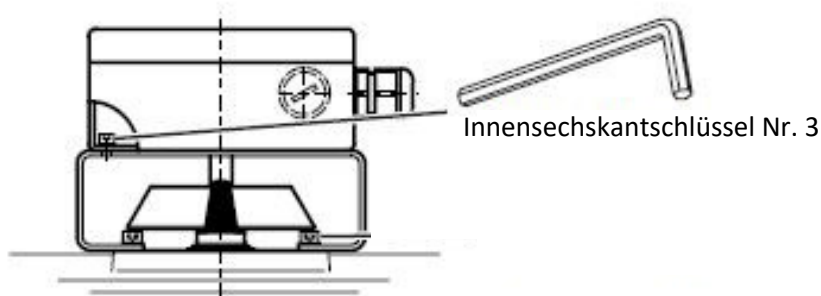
zeigt die Befestigung des Schaltkastens auf der VDI/VDE Brücke.
